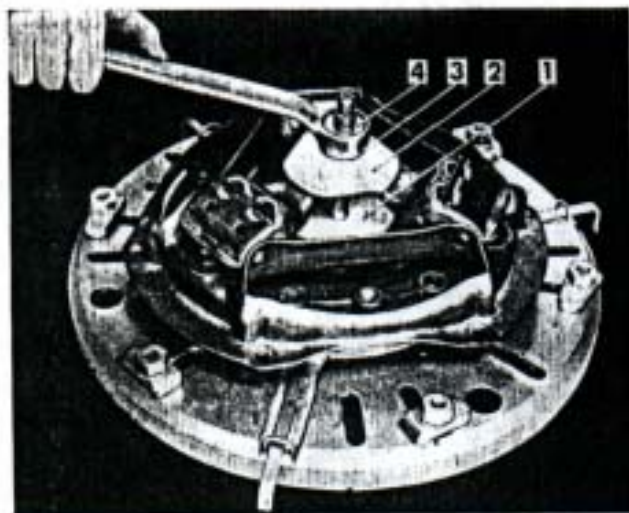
Desarmando el embrague "AUBURN" en el plato HS-64.
